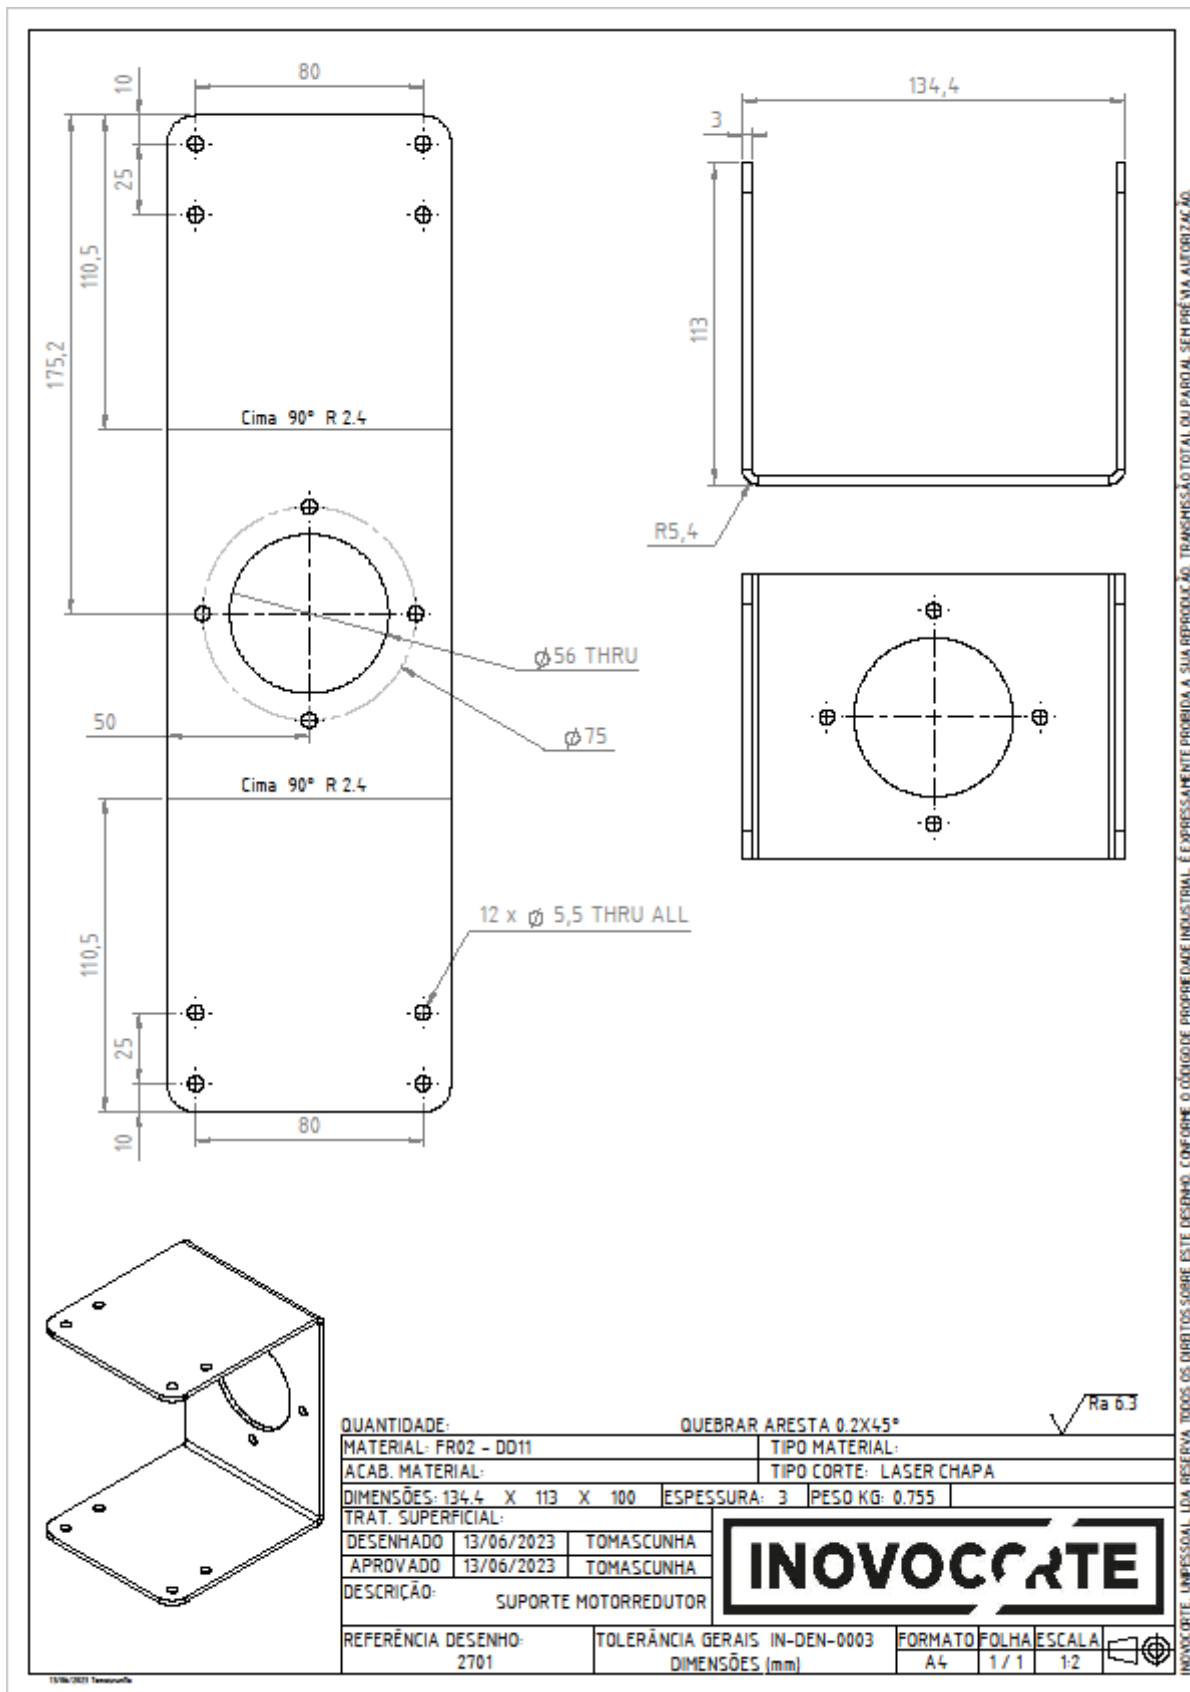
Desenho técnico do suporte motorreductor (2701).
